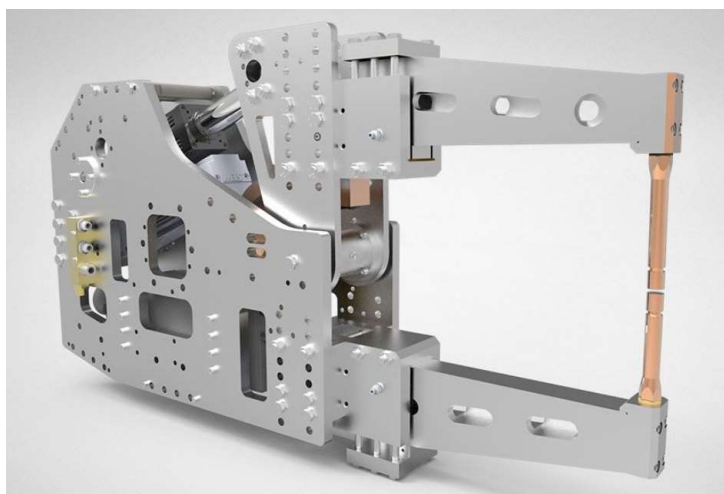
Svařovací kleště Flexgun UL-C[18]
